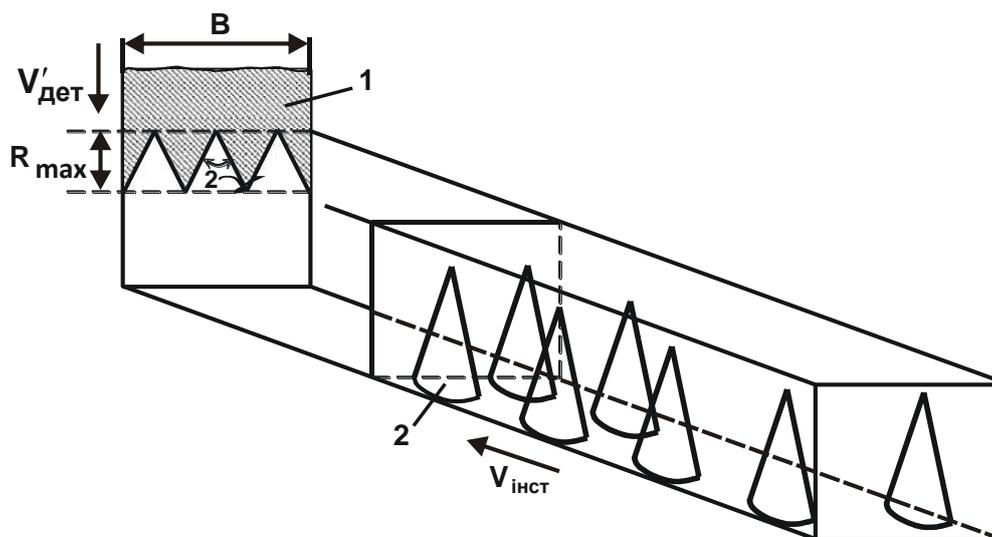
Схема формування шорсткості плоскої поверхні під час алмазно-абразивної обробки
